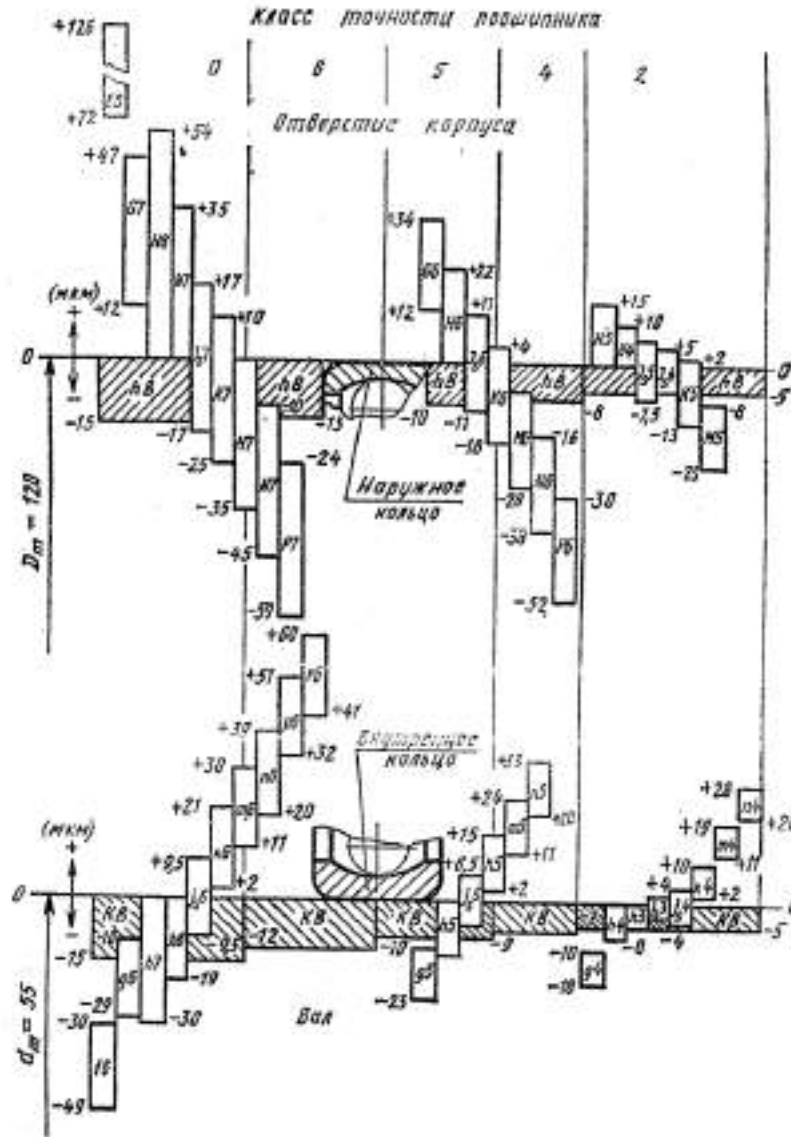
Схемы расположения полей допусков на диаметры колец подшипников качения, отверстий в корпусах и валов
